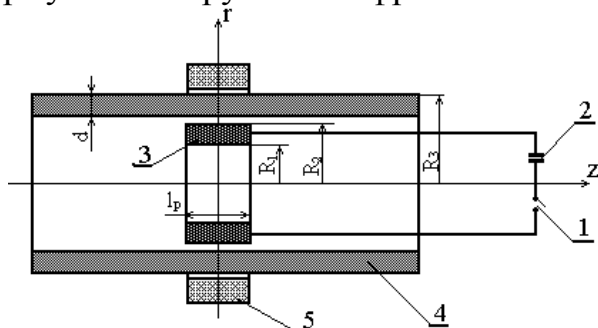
Модель індуктора для роздачі циліндричної труби: 1–комутатор; 2–накопичувач; 3–індуктор; 4–заготовка; 5 – матриця
